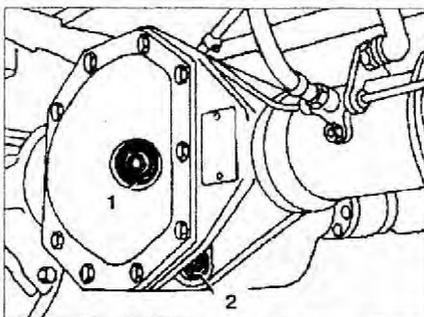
б. Редуктор задней оси 741.13 (HL 0):
